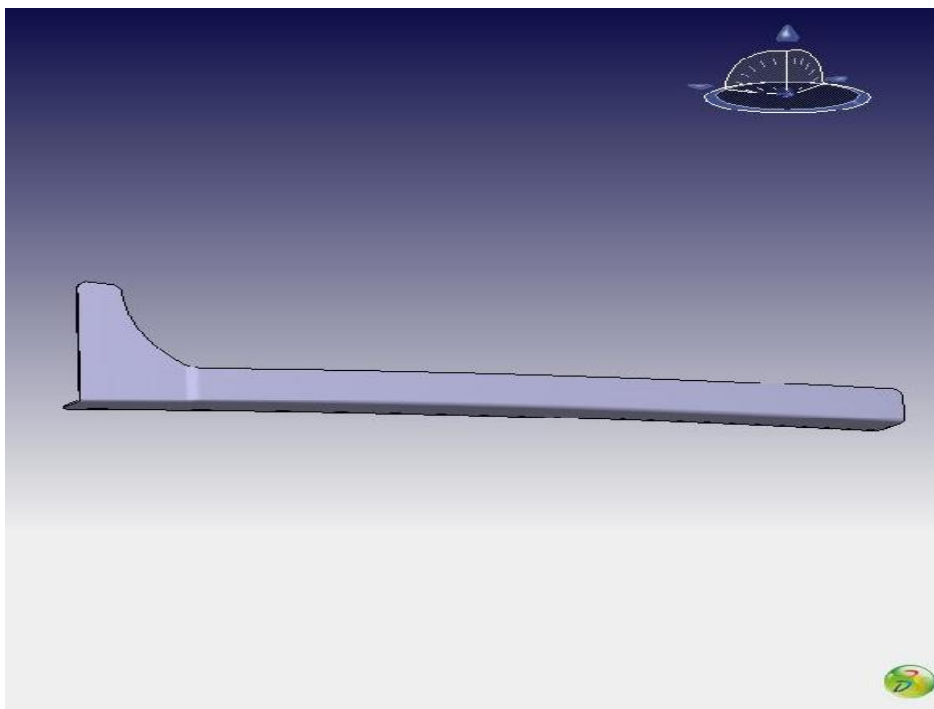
Exemplo do suporte inferior de ligação das vigas e batente do vidro.
